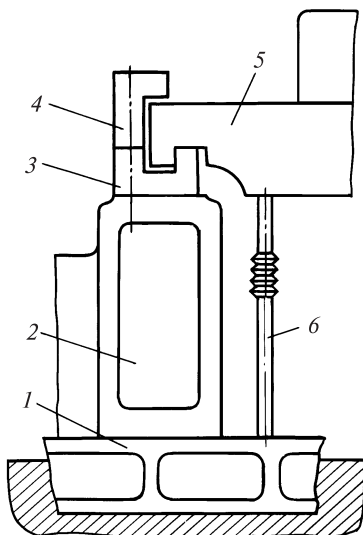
Установка дополнительной опоры под лапу для уменьшения силы, действующей со стороны лапы на корпус подшипника
